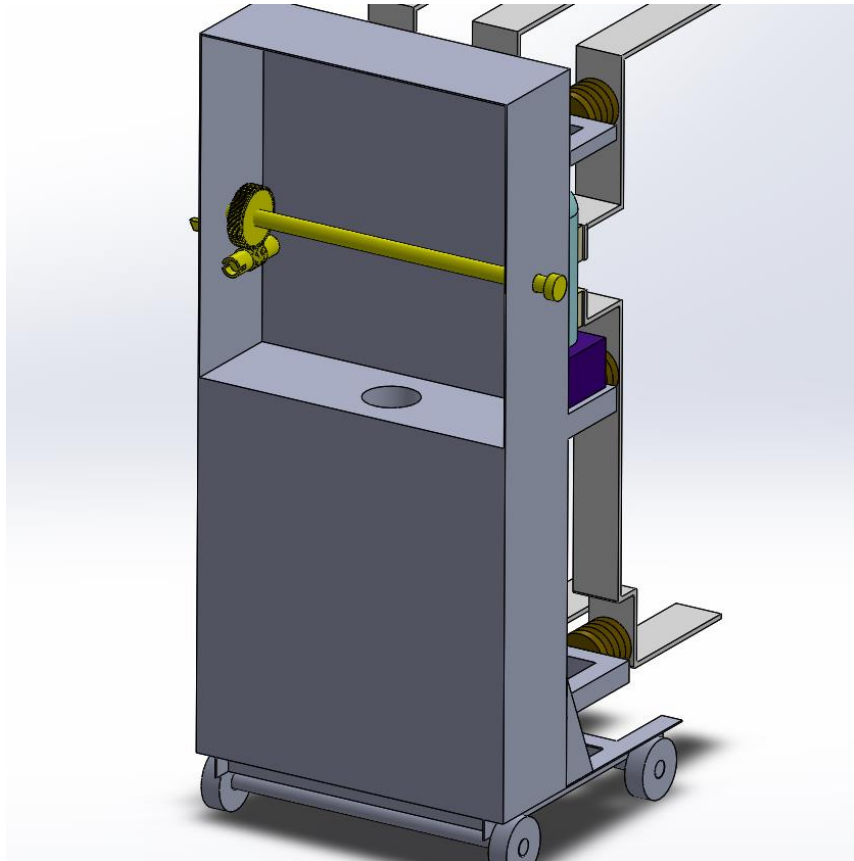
Головний вал вкочування візка, змодельований в САПР SolidWorks в корпусі візка вимикача
